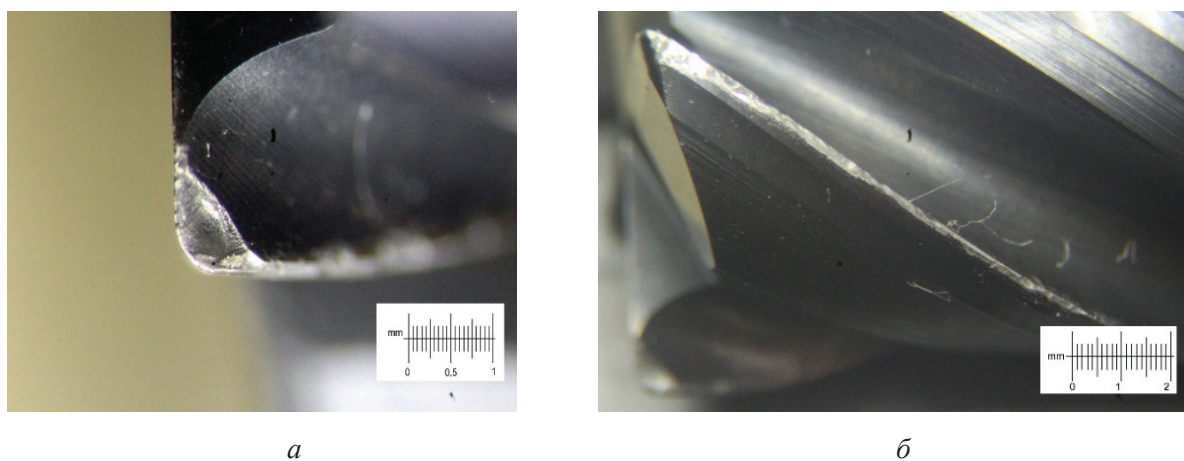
Фотография износа фрезы № 3 по передней (а) и задней (б) поверхности
